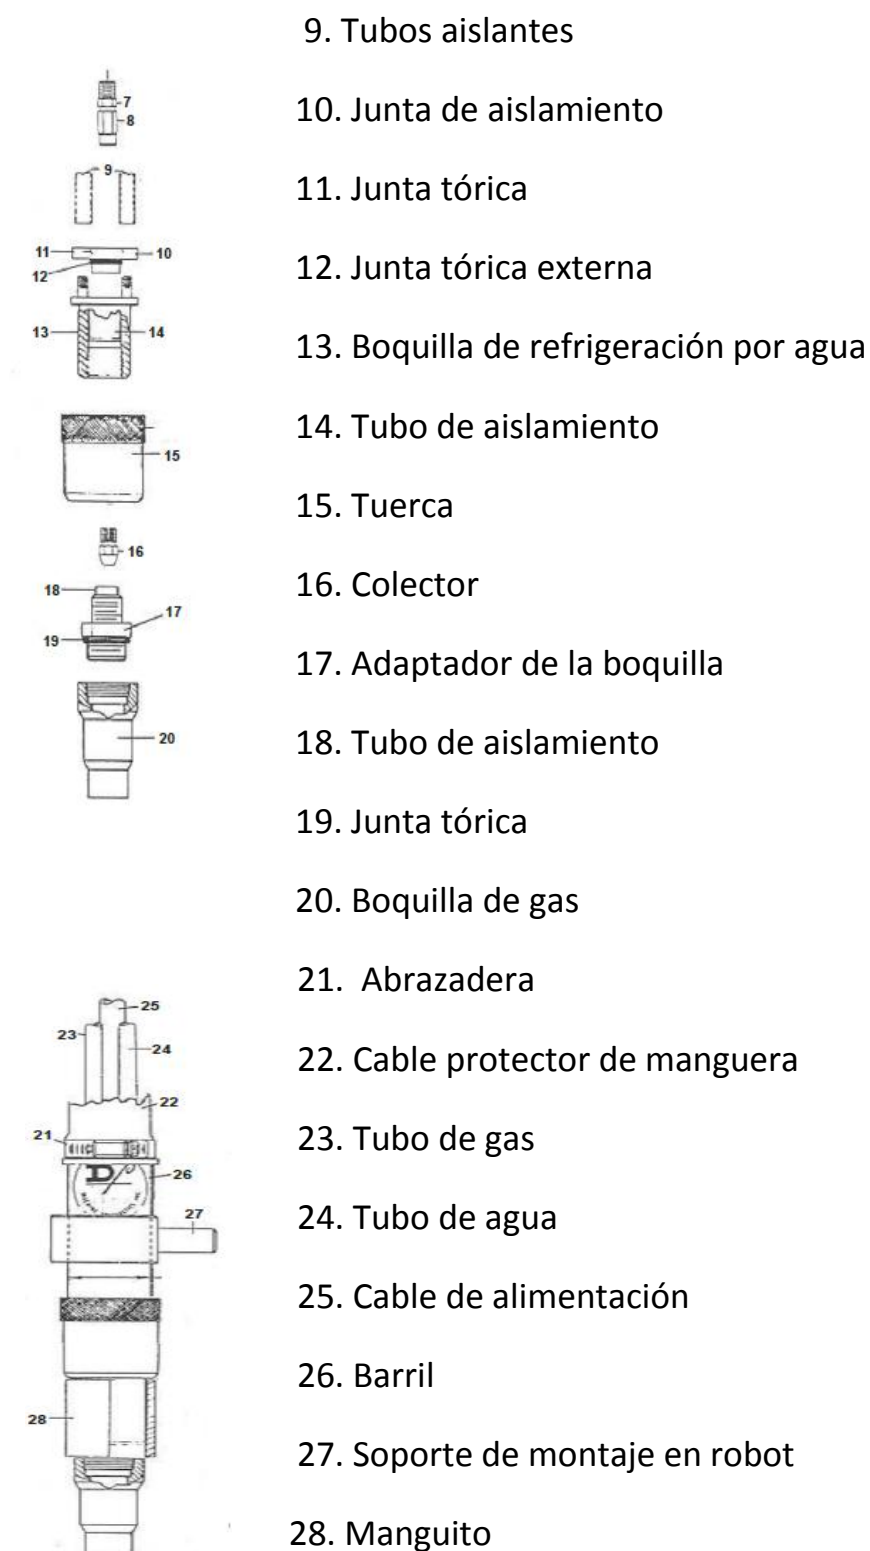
Estructura de una pistola TIG (DF Machine specialities, 2014)
